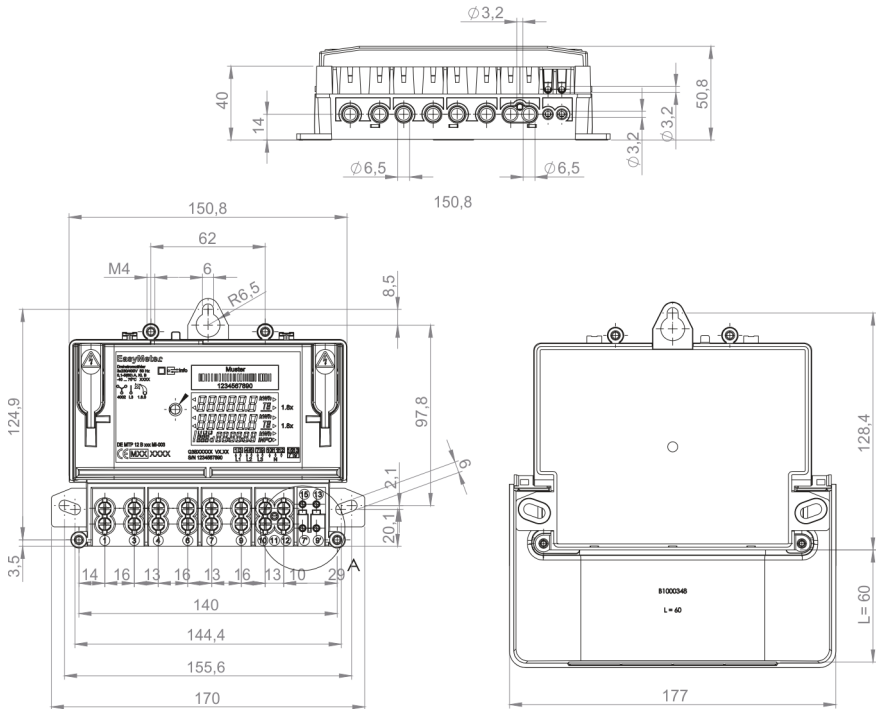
Maßblatt (60-Ampere-Ausführung mit 6,5-mm-Klemmen)
